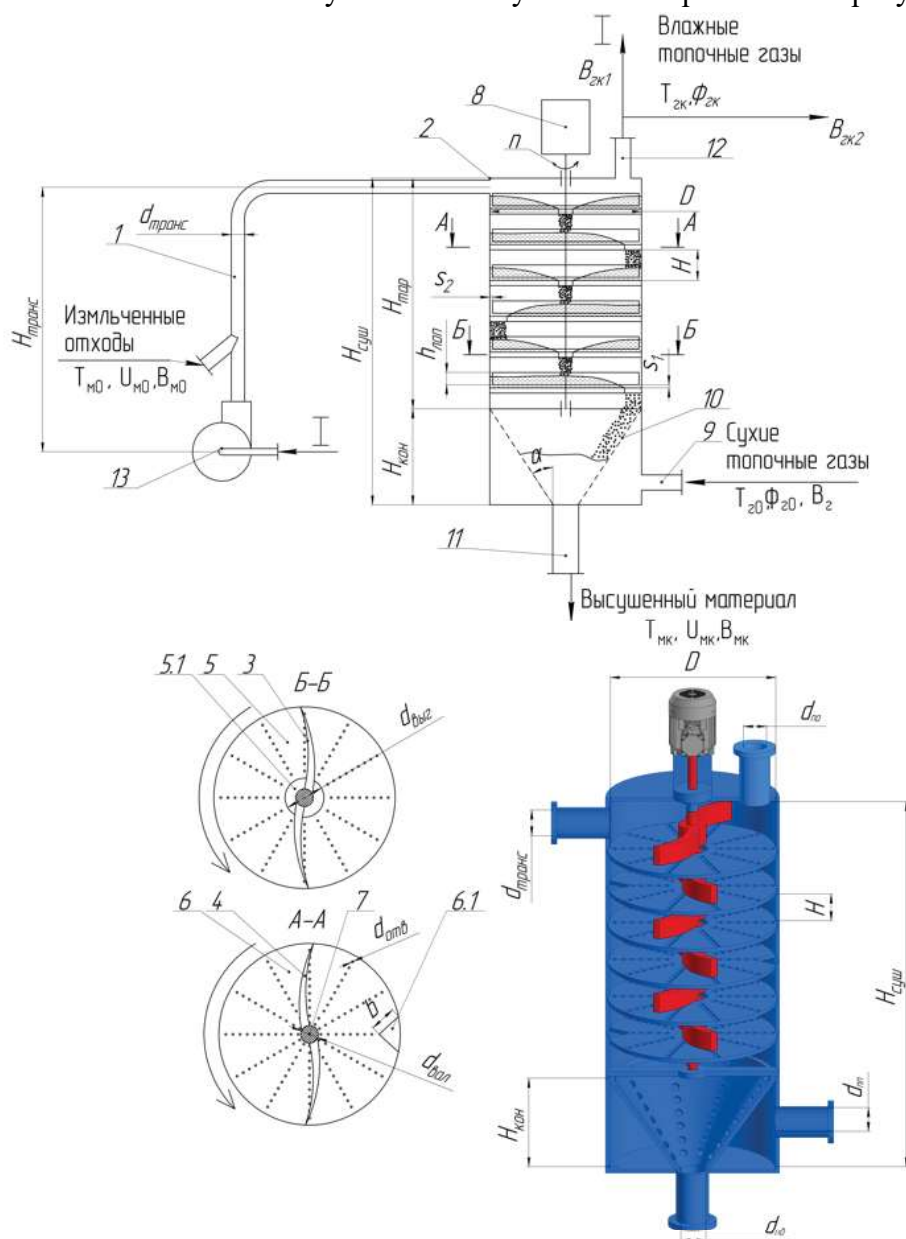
Схема и внешний вид лопастной сушилки с радиальным движением материала
